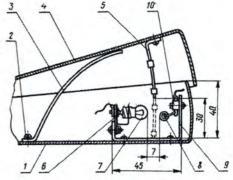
Конструкция пебали. 1 — корпус; 2 — винт крепления пружины; 3 — плоская пружина; 4 — крышка; 5 — кронштейн с экраном переменной прозрачности; 6 - держатель лампы накаливания; 7 — лампа накаливания 3,5 B/0,26 A; 8 — диод Д2В; 9 — скоба крепления лампы и диода; 19 -- изолятор-держатель дио-
